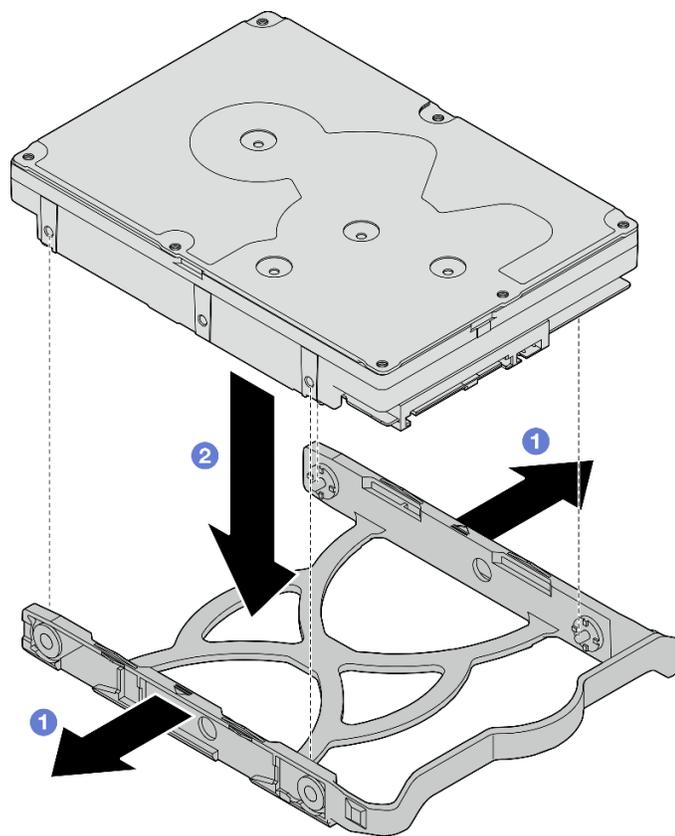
Установка 3,5-дюймового диска в фиксатор
